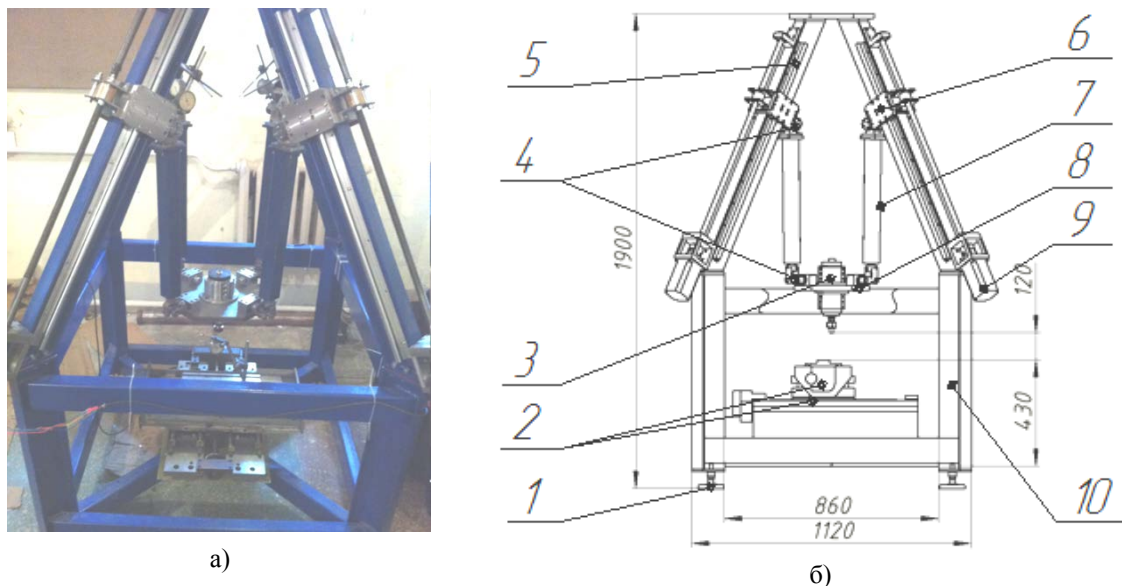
Свердлильно-фрезерний верстат пірамідальної компоновки: а – фото; б – схема – опора 1, хрестовий стіл 2, мотор-шпиндель 3, шарнір 4, напрямна 5, каретка 6, штанга постійної довжини 7, рухома платформа 8, лінійний двигун 9, каркас 10 .
